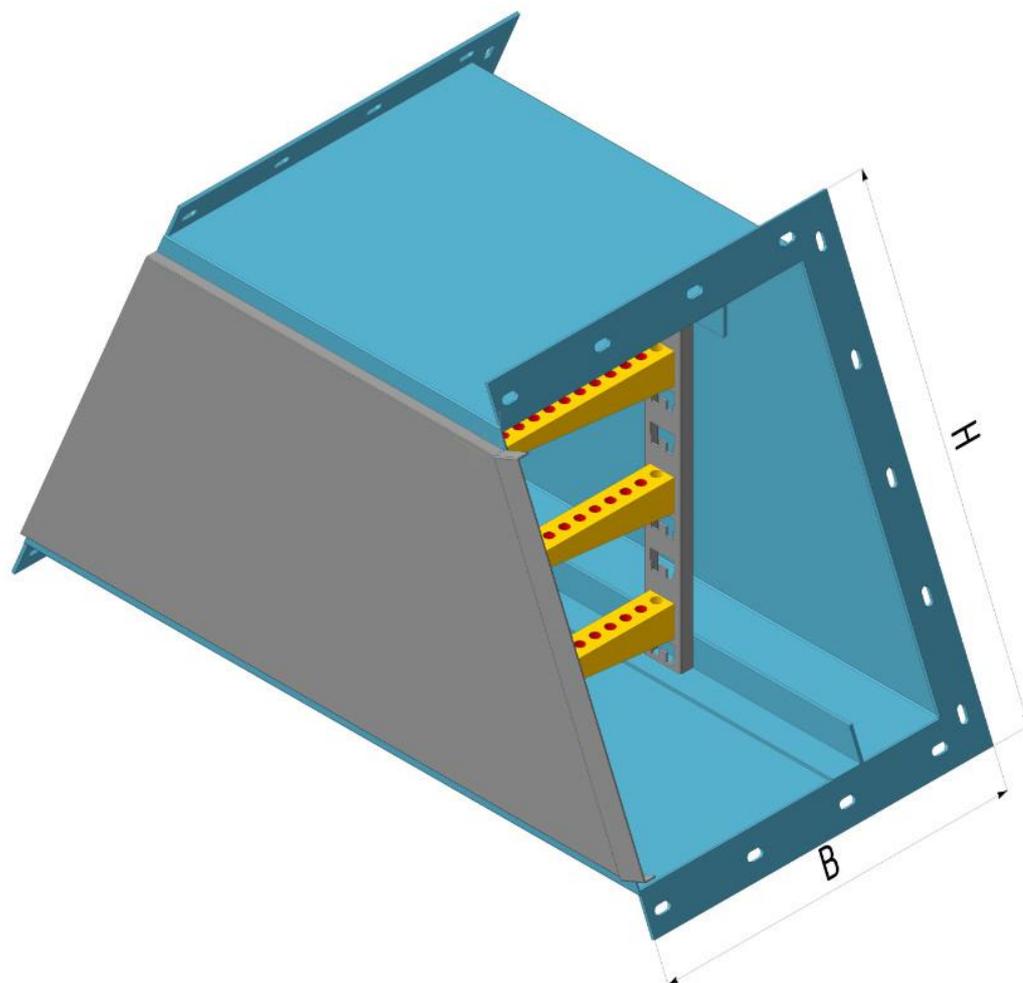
Короб кабельный блочный угловой с поворотом вверх типа ККБ-УВ. Общий вид
